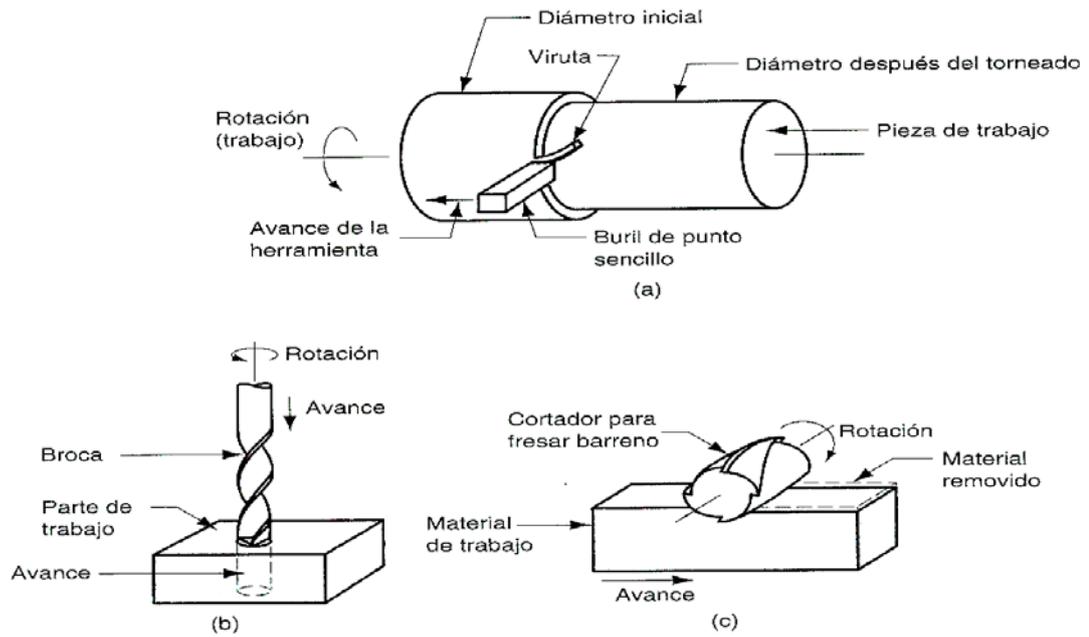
Operaciones comunes de maquinado; a) torneado, en el cual un buril de punto sencillo remueve material de una pieza de trabajo giratoria para reducir su diámetro; b) taladrado, donde una broca rotatoria avanza dentro del material para generar un barreno redondo; c) fresado, en el cual se hace avanzar un material de trabajo por medio de un cortador giratorio con filos múltiples.
